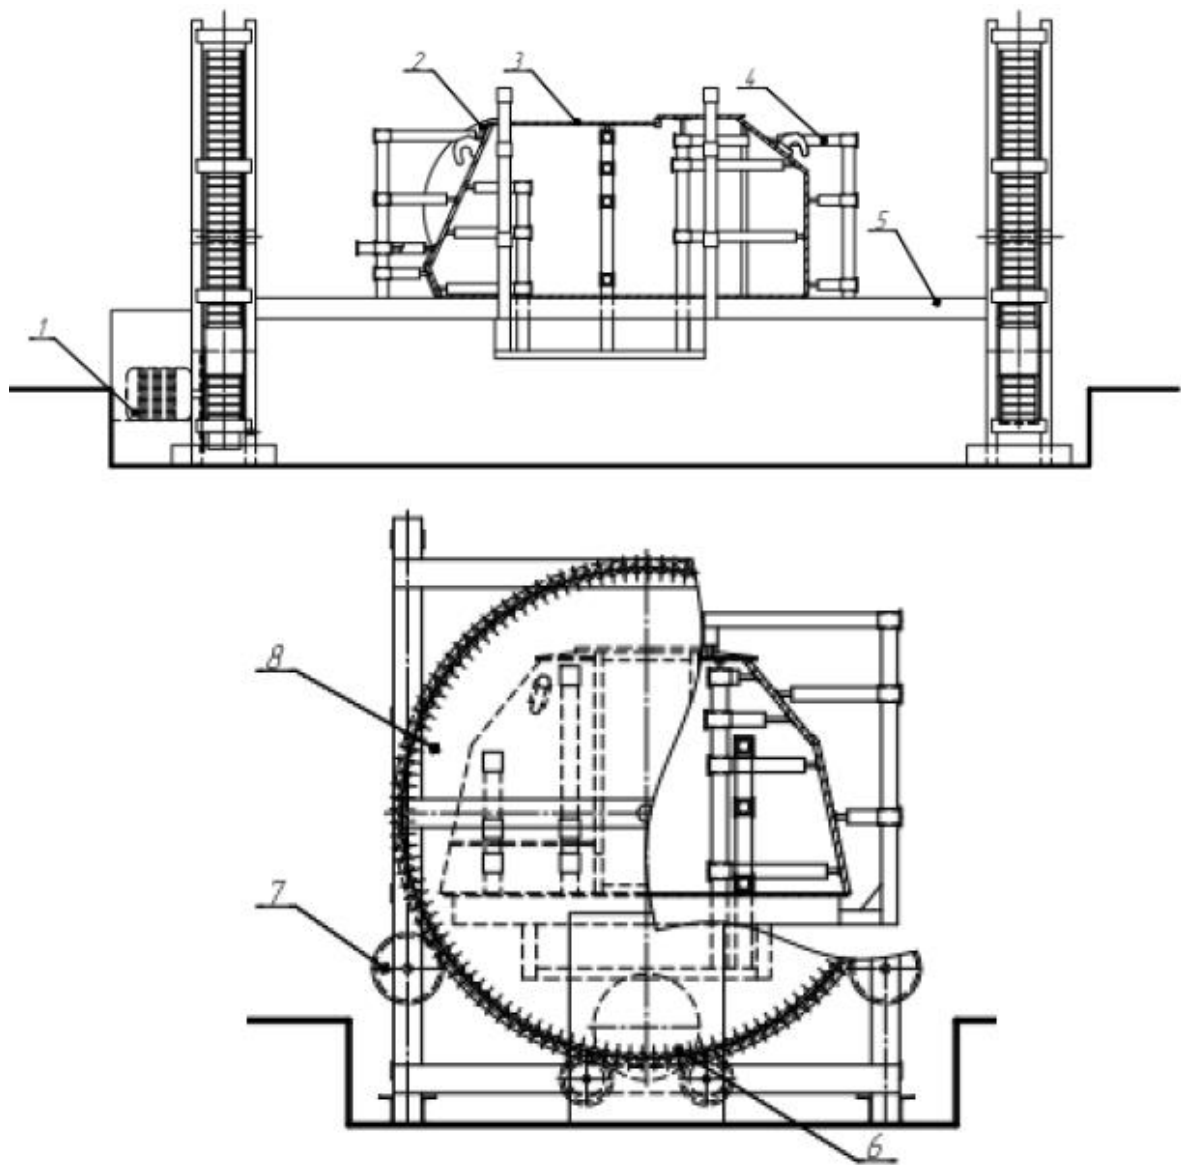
Складально-зварювальний стенд корпусу типу «Ковпак»:
